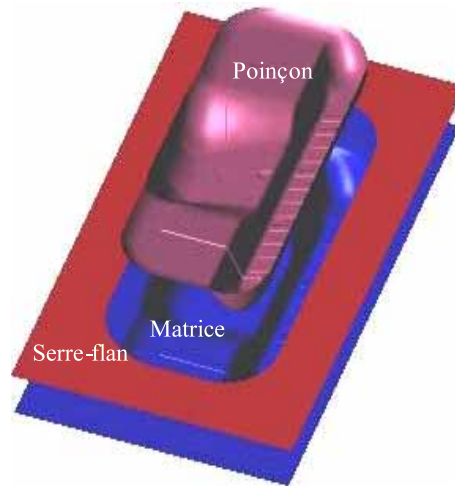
CAO des outils rigides du cas d’emboutissage Craft-Fastool
